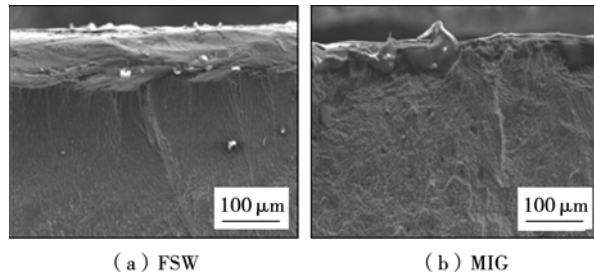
6082 铝合金 FSW 及 MIG 焊宏观疲劳断口形貌
